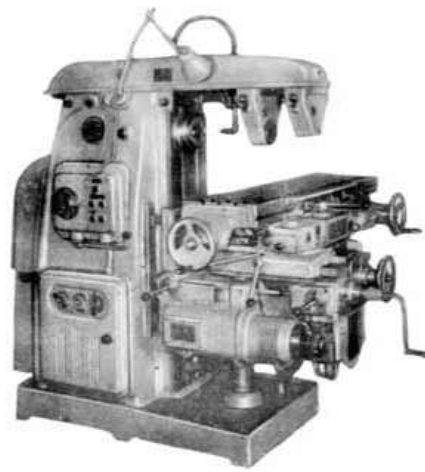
Консольно-фрезерный станок 6М82
